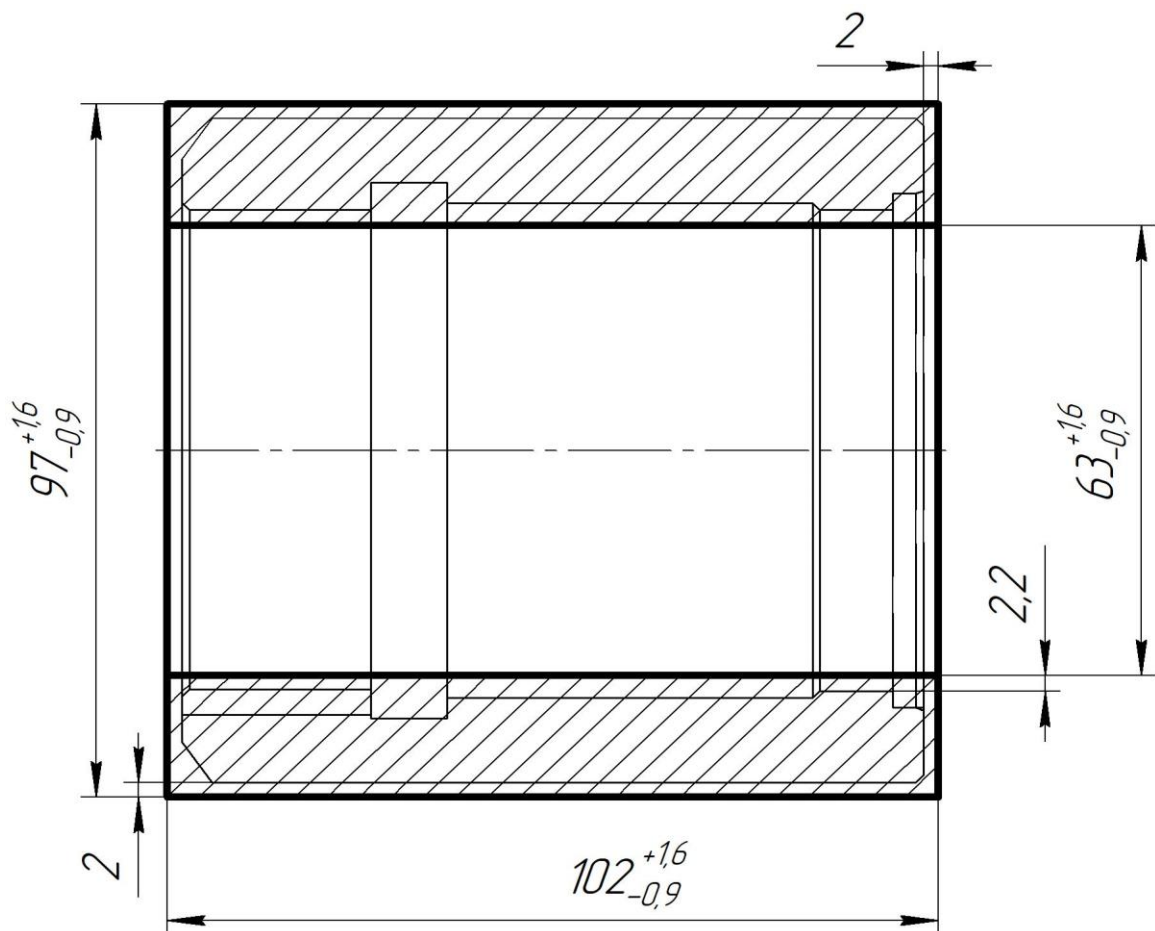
Креслення заготовки барабан за методом КГШП
